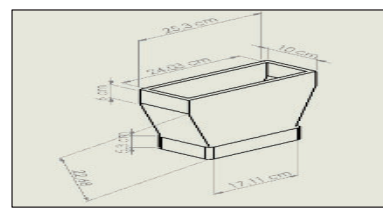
Plano Pieza 3: dispensador de Jabón. Fuente: Elaboración propia
